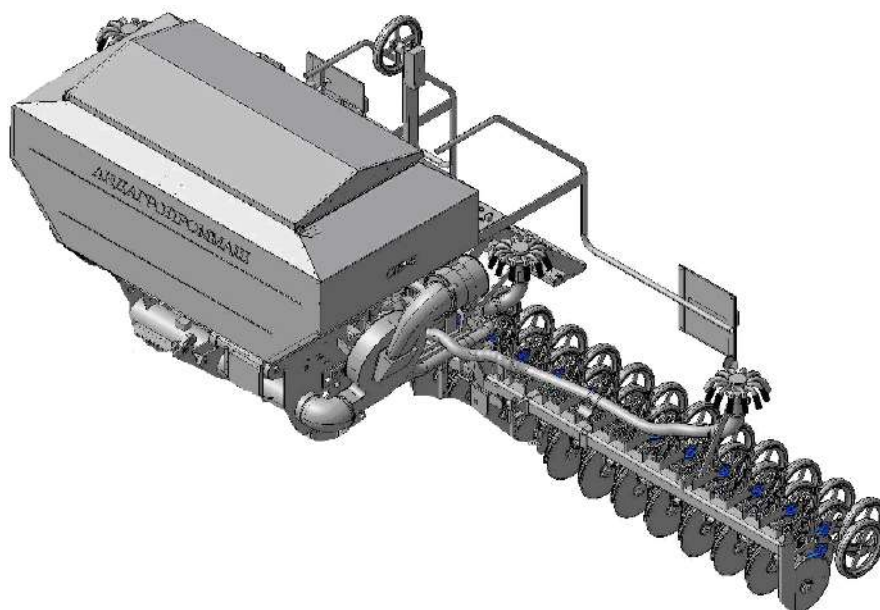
Общий вид сеялки пневматической рядной СПР
